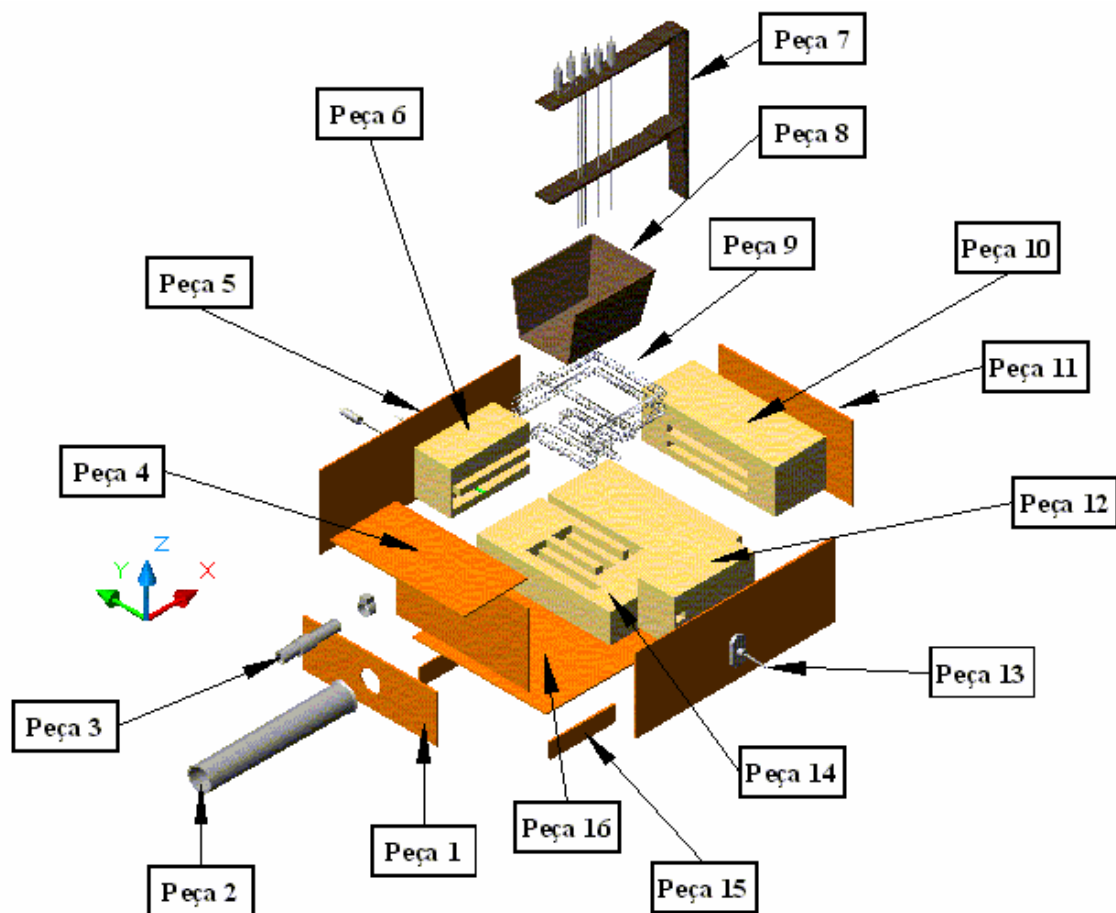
Vista geral do conjunto de peças componentes do dispositivo de solidificação utilizado neste trabalho.
